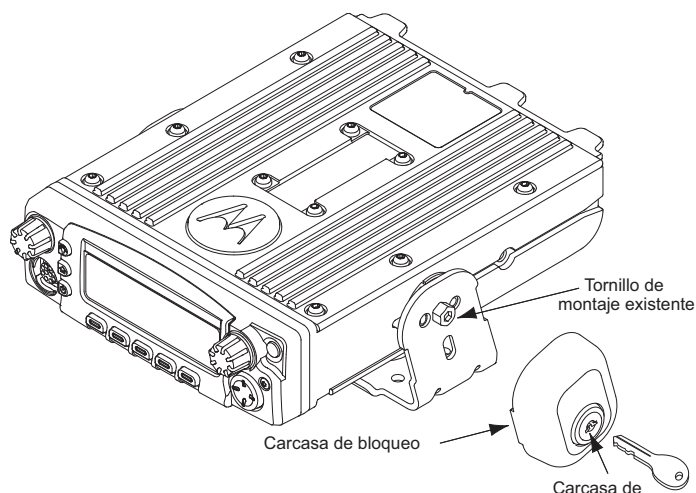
Kit de cerradura (opcional) (no puede utilizarse en radios de 100 W)
